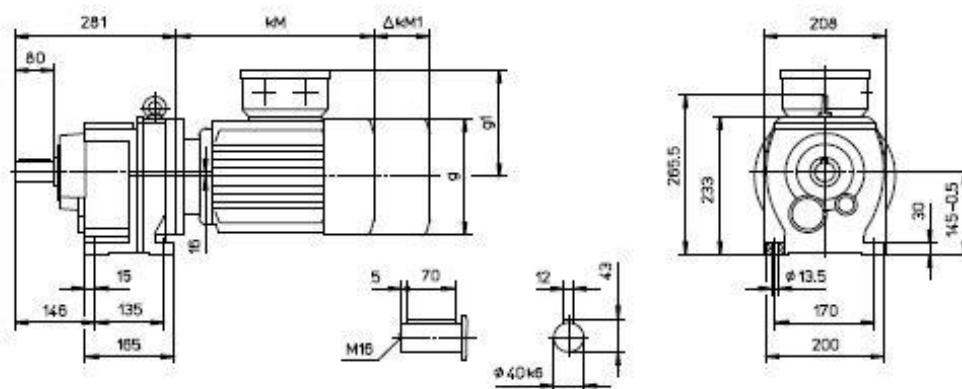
Габаритные и присоединительные размеры мотор – редуктора G93G42A DM90S4
